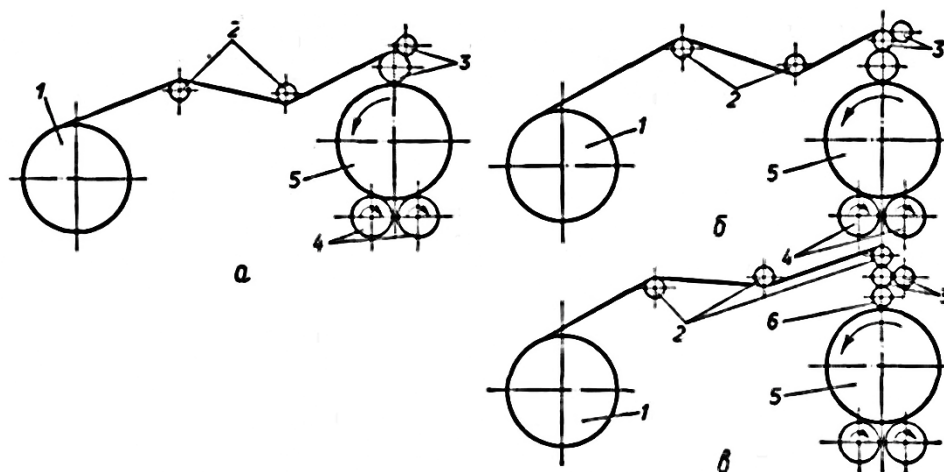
Схемы продольно-режательных станков с верхней заправкой: а – с ножевым валом; б – с ножевым валом и отдельно расположенным прижимным валом; в – с отдельно расположенными ножами, бумаговедущими валиками и прижимным валом; 1 – раскат; 2 – бумаговедущий валик; 3 – механизм продольной резки; 4 – несущие валы; 5 – наматываемый рулон; 6 – прижимной вал
